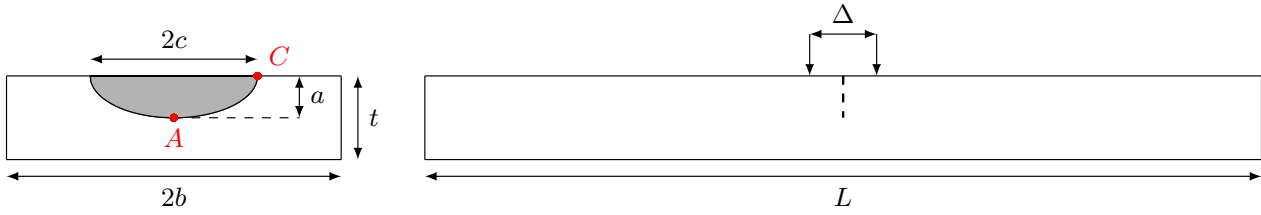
Dimensions caractéristiques de la géométrie d'une éprouvette SCT
